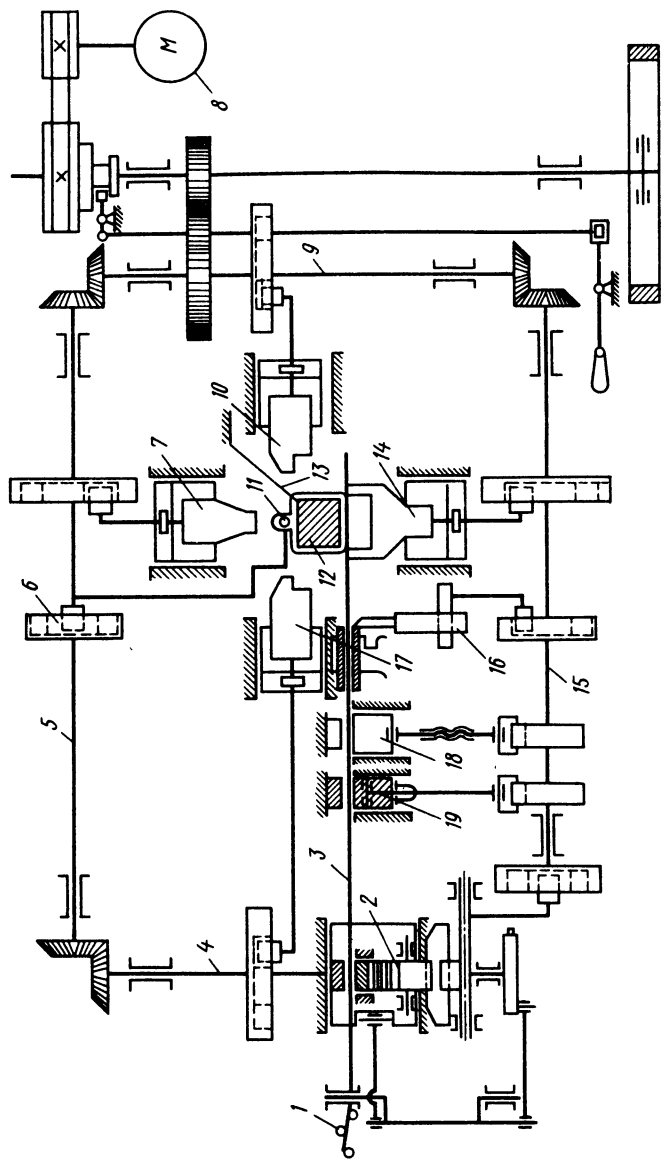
Кинематическая схема четырехползунного универсально-типичного автомата:
